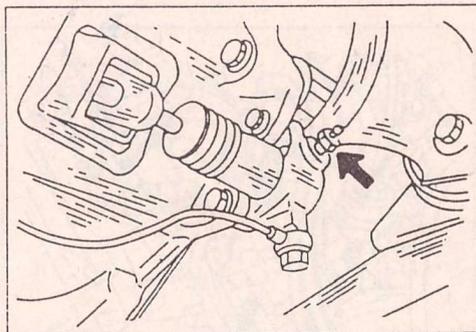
Исполнительный гидроцилиндр привода сцепления. Стрелка указывает на вентиль выпуска воздуха.
